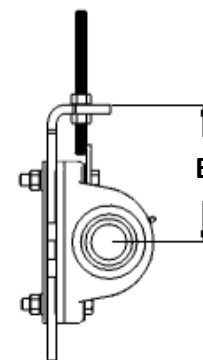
Paddle Shaft для лифтера Колесо Кольцо Измерение
